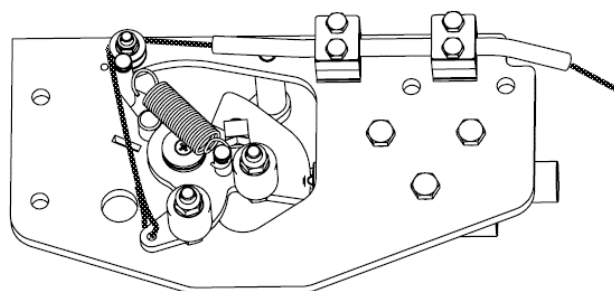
Module de démarrage du coupe-film – position ouverte du coupe-film.
